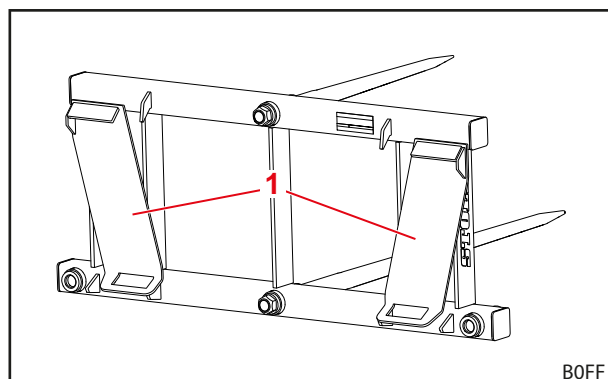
Konstrukcija šiljka za bale H – pogled sprijeda
